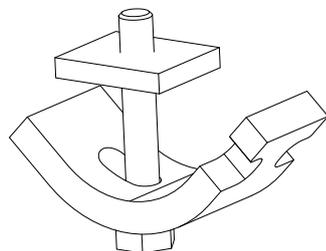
Griffes de serrage, résistantes à la torsion, épaisseur de serrage 6-25 mm (acier galvanisé)
